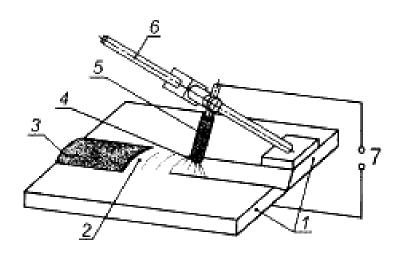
Гравитационная сварка покрытым электродом 1-заготовка; 2-сварной шов; 3-шлак; 4-дуга;5-покрытый электрод; 6-направляющая;7-источник питания
